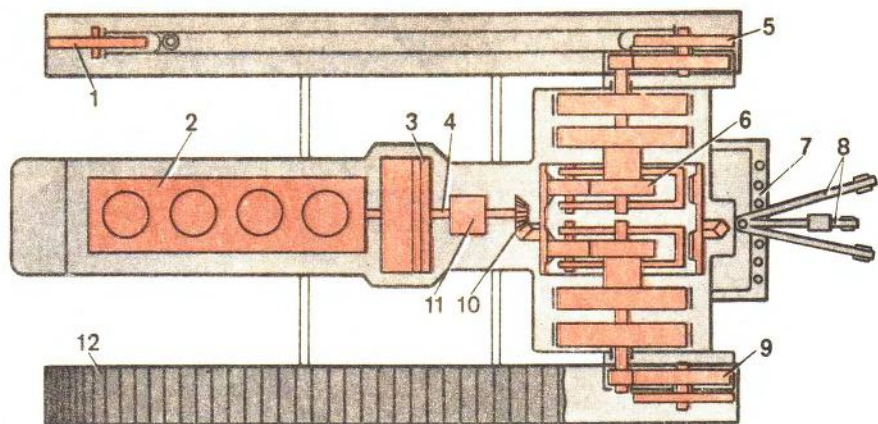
Расположение основных частей, их механизмов и деталей гусеничного трактора ДТ-75МВ:
